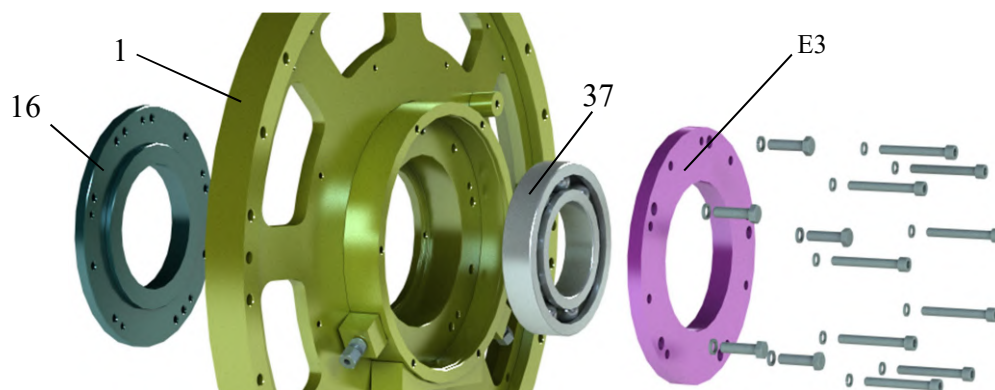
Демонтаж деталей из подшипникового щита (сторона привода)
